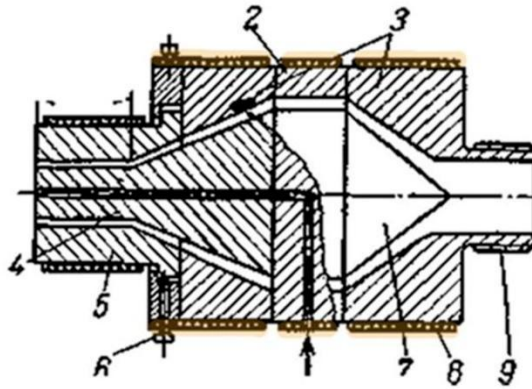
1 – зона «заспокоєння» потоку; 2 – дорнотримач; 3 – корпус; 4 – дорн; 5 – мундштук; 6 – центрувальний гвинт; 7 - голівка дорна; 8 – нагрівач; 9 – різьблення для приєднання голівки до екструдера
